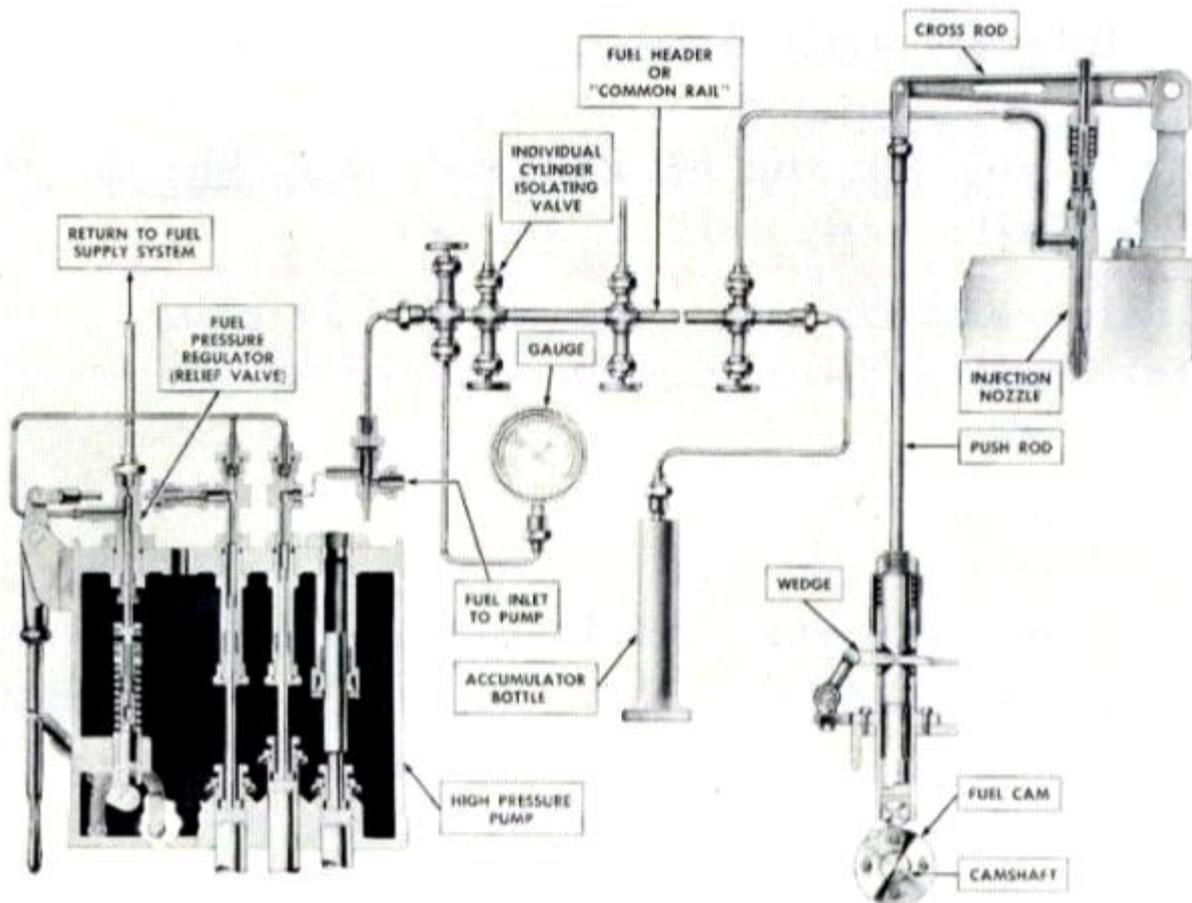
Схема ТПСАТ двигателей Atlas Imperial Diesel Engine Co.
